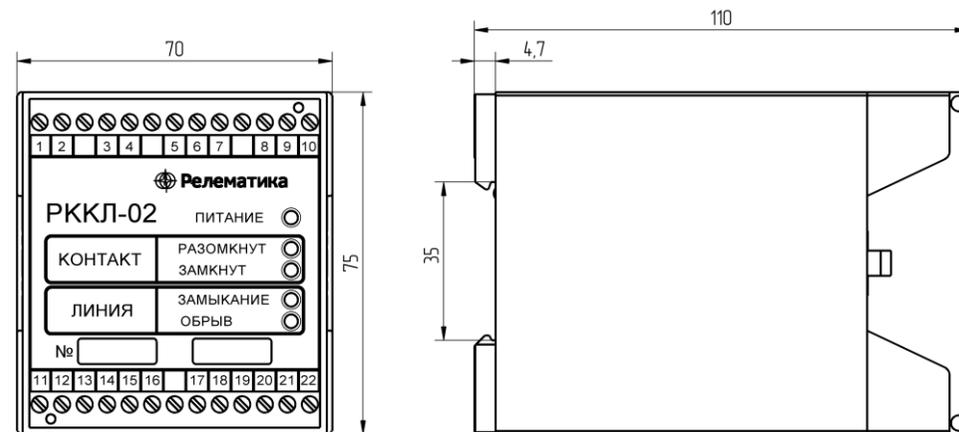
Внешний вид и габаритные размеры блока реле РККЛ-02
